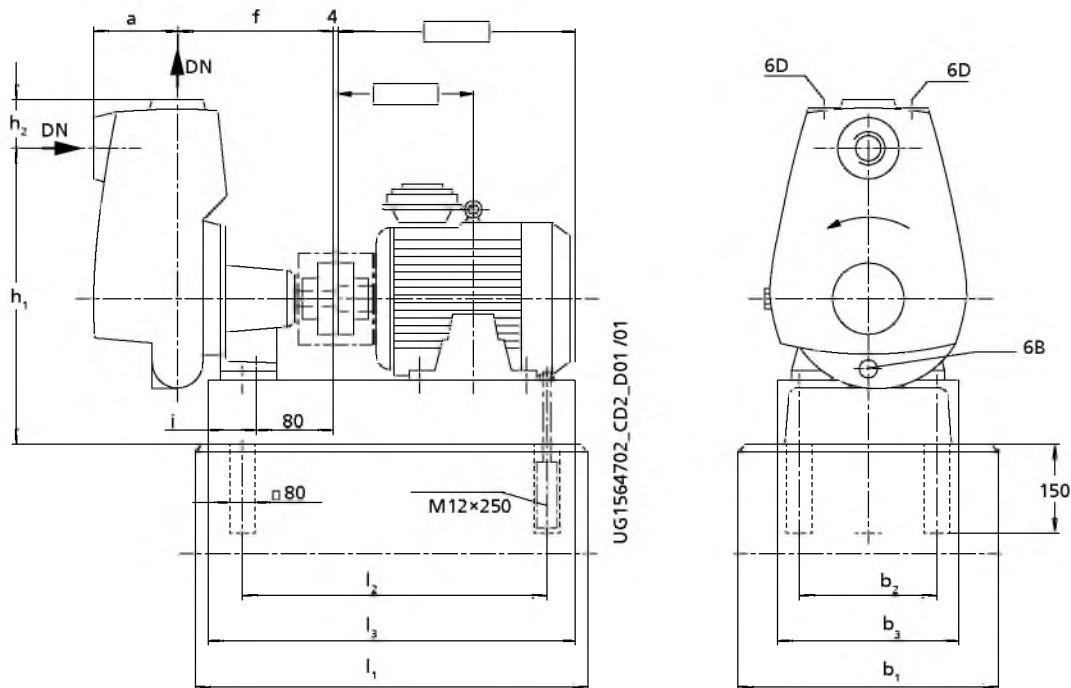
Габаритные размеры типоразмер 025-025-100 до 040-040-110 (узел вала 17) – насосный агрегат
